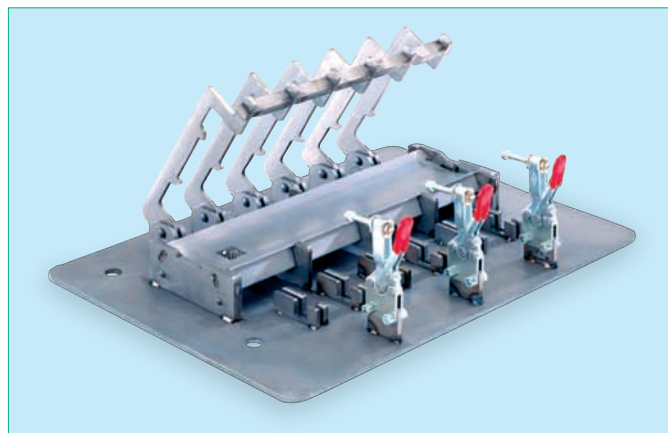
Фиксирующая оснастка для лазерной сварки
